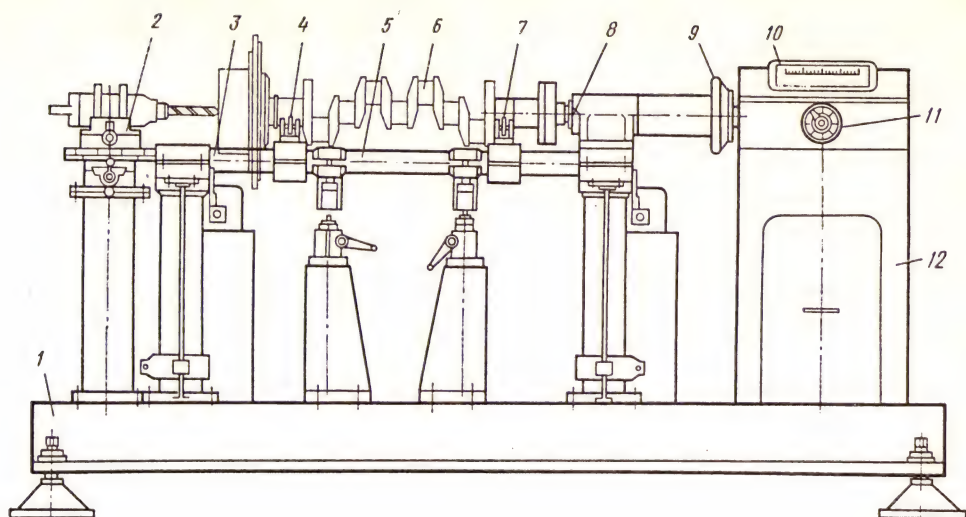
Станок для динамической балансировки коленчатого вала:
